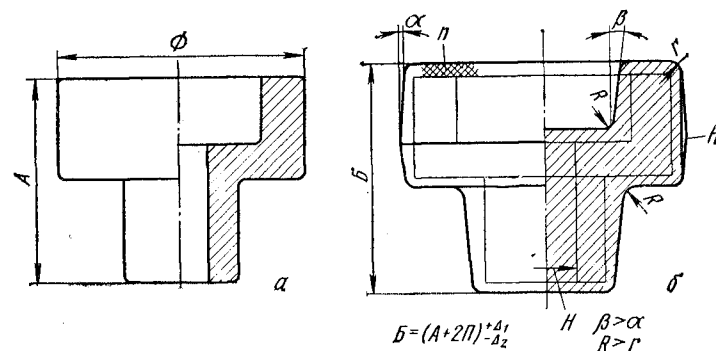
Пример составления по чертежу детали (а) чертежа поковки (б): 1 — плоскость разреза; Δ — отклонения от номинального размера; H — напуск; P — припуск на механическую обработку; α и β — штамповочные (наружные и внутренние) уклоны; r , R — наружные и внутренние радиусы закруглений; A , D — номинальные размеры детали; B и D_1 — номинальные размеры поковки
